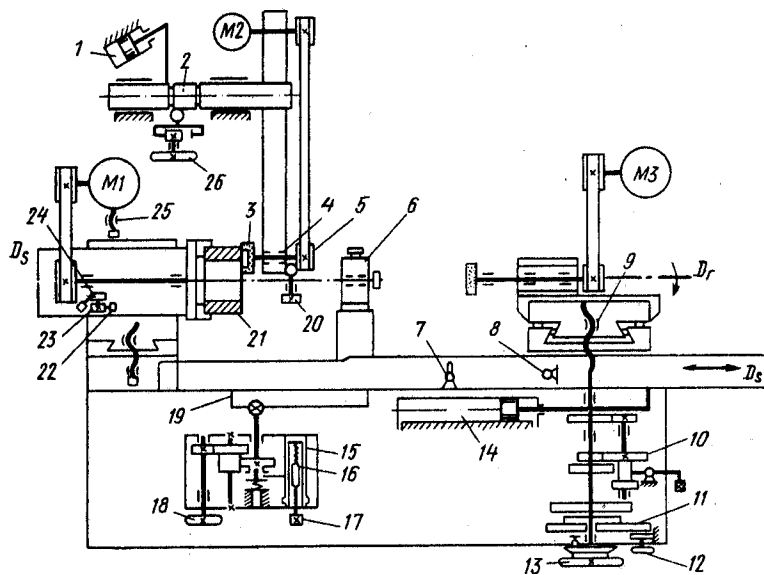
Кинематическая схема внутришлифовального станка мод. 3К227В
